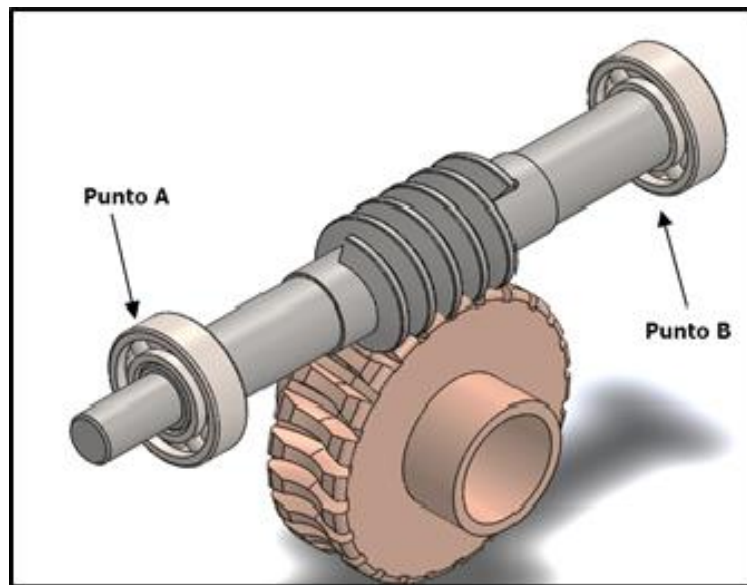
Vista isométrica, puntos que se someten a cargas del sistema de transmisión.
